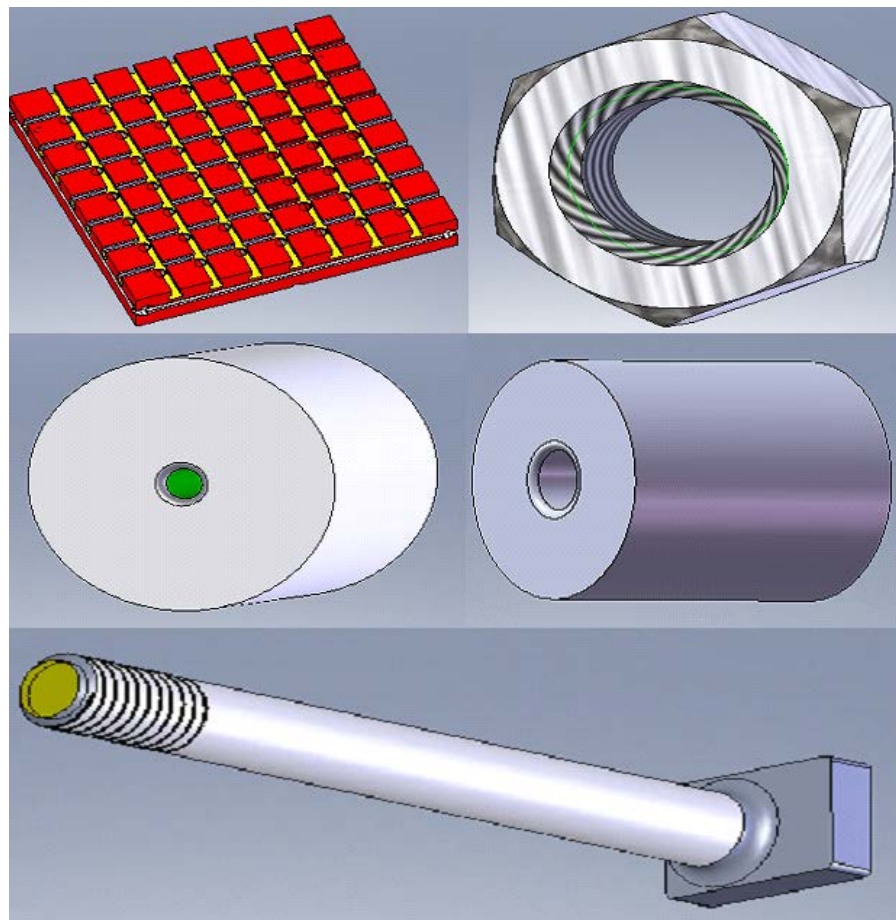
Елементи пристосування для обробки «Корпус».
